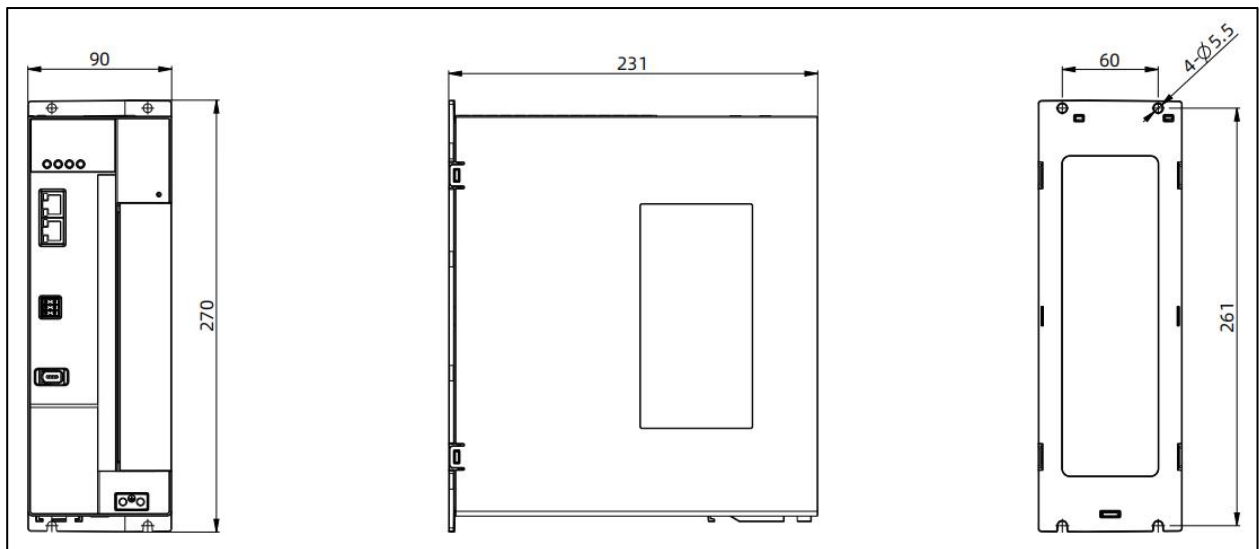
Size D 伺服驱动器安装尺寸 (单位: mm)
